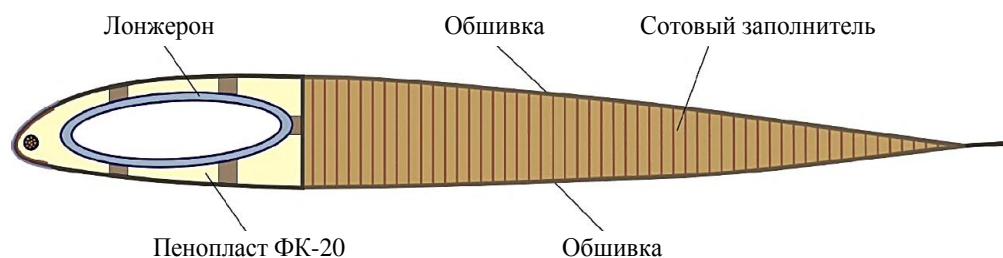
Поперечное сечение смешанной конструкции лопасти несущего винта вертолета
